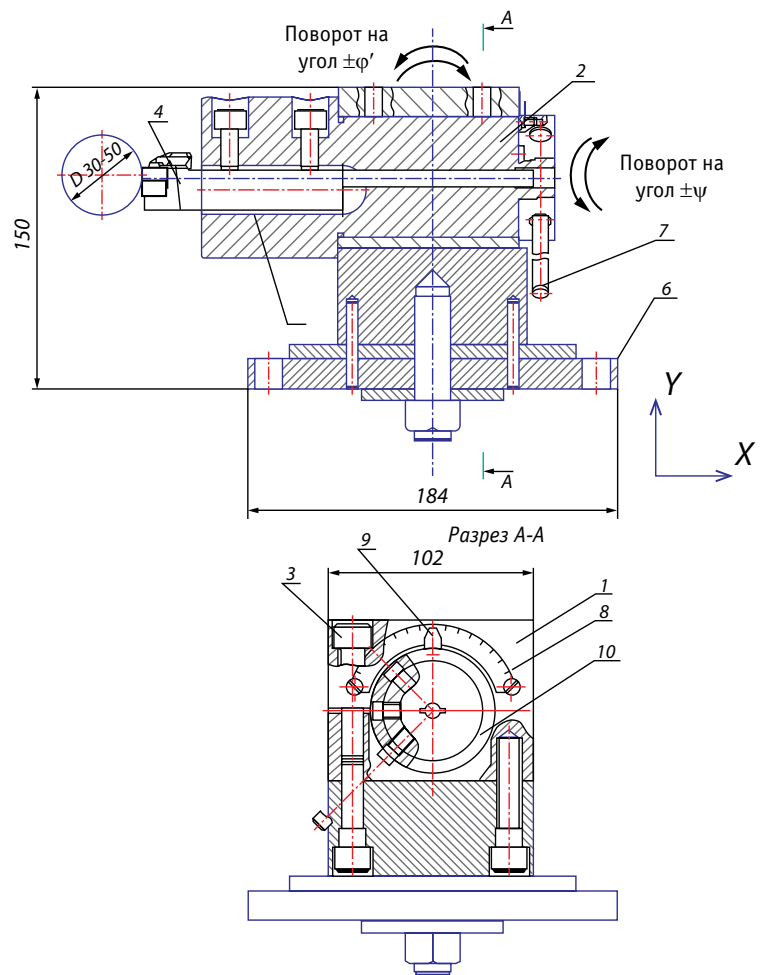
Сборочный чертеж технологического приспособления для обработки выглаживанием с применением СМП
